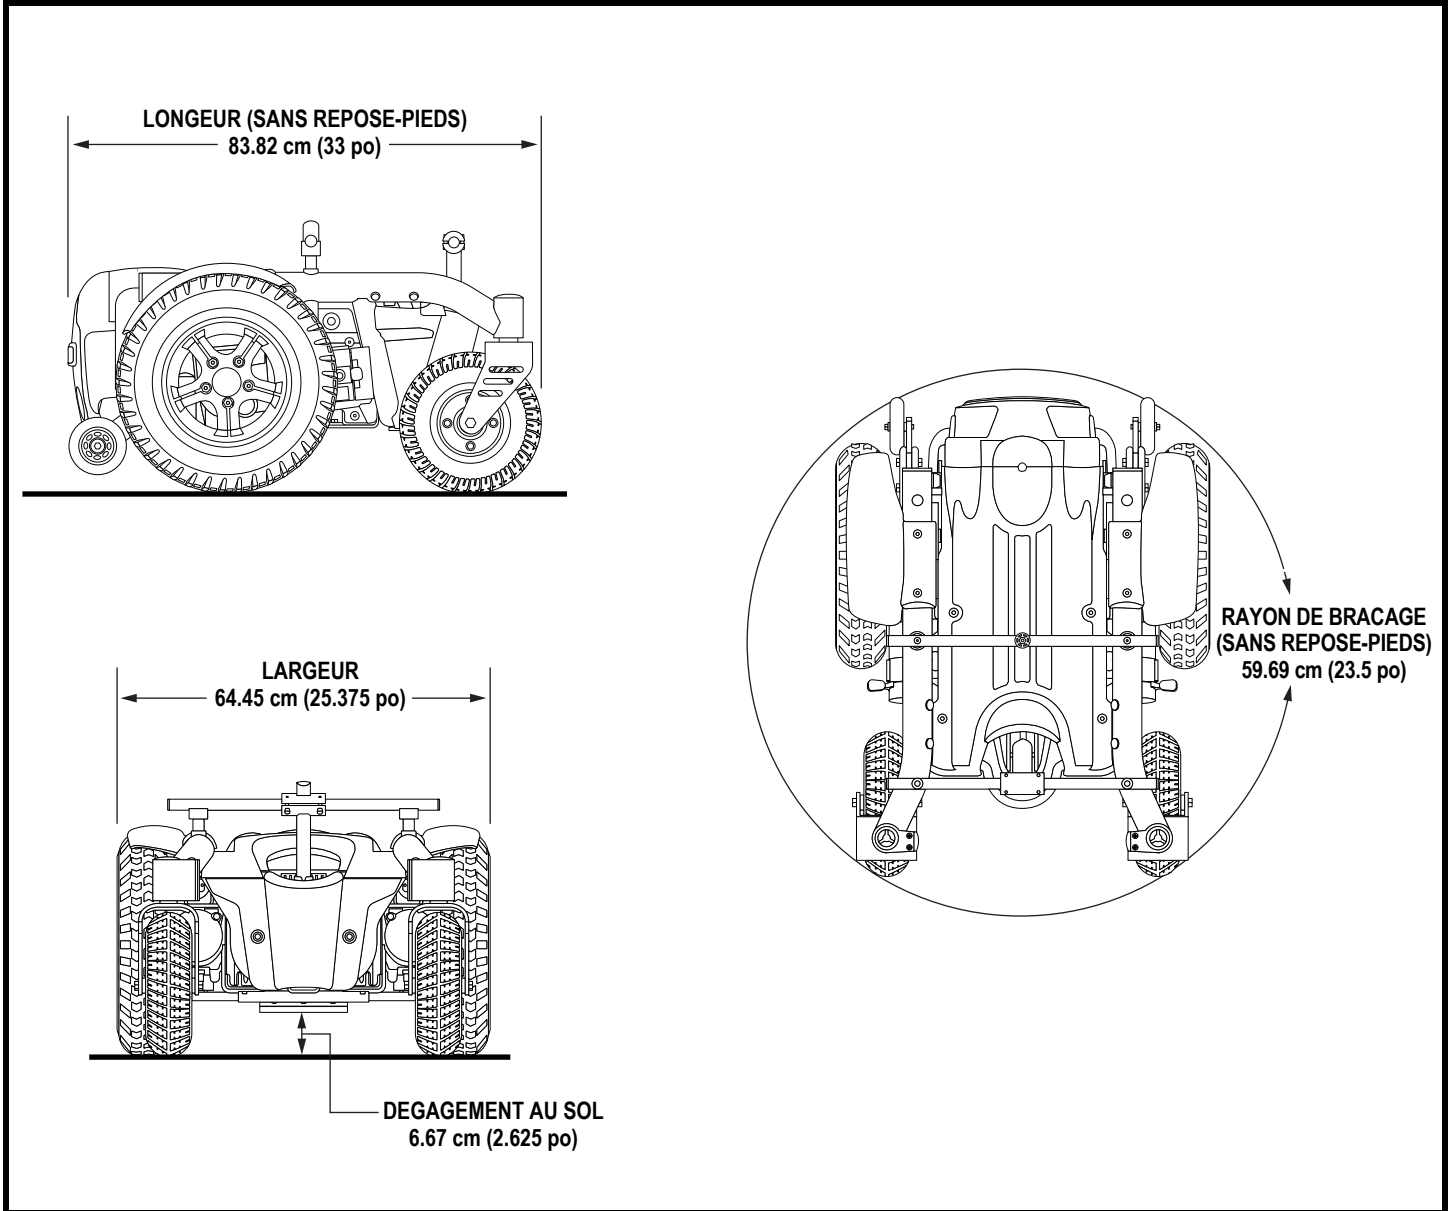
Quantum Vibe R-4000 Dimensions et dégagement au sol
